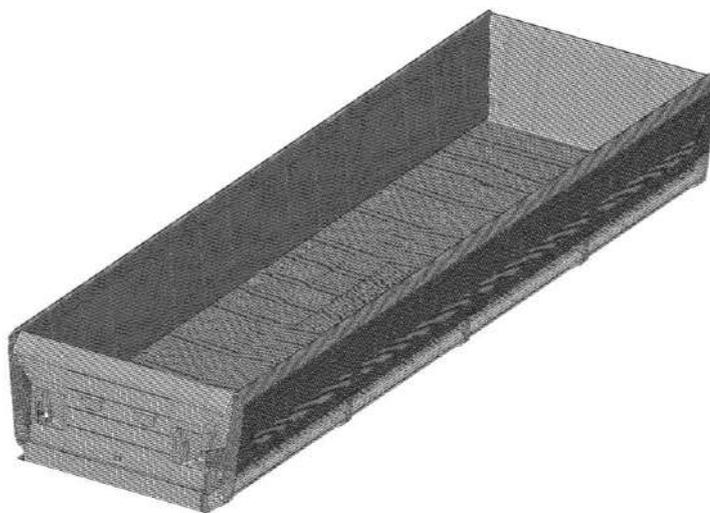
Детализированная пластинчатая конечно-элементная модель несущих конструкций кузова вагона-самосвала
